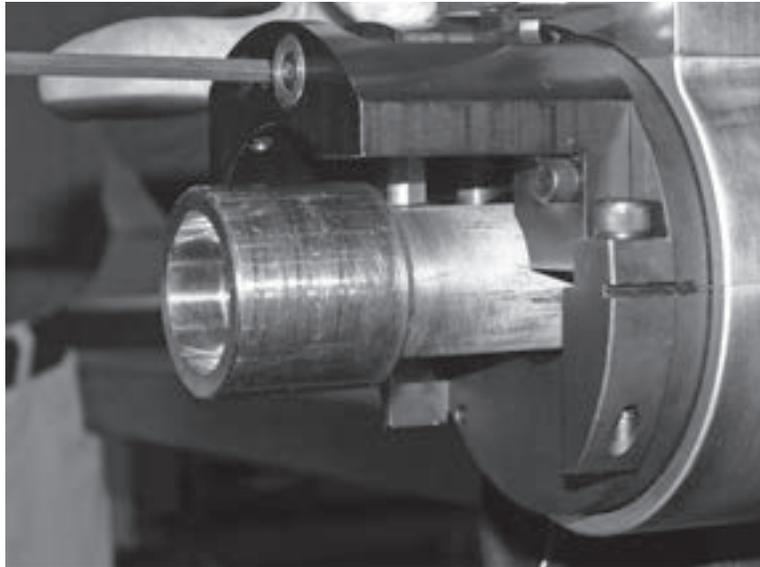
Das Foto zeigt den Werkzeugschlitten zum axialen Trennen von Muffenschweißnähten in der Position zur Entfernung der Muffenschweißnaht.
